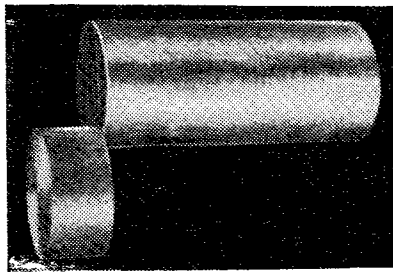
Сдвиг отрезаемой заготовки при закрытой резке с осевым сжатием
